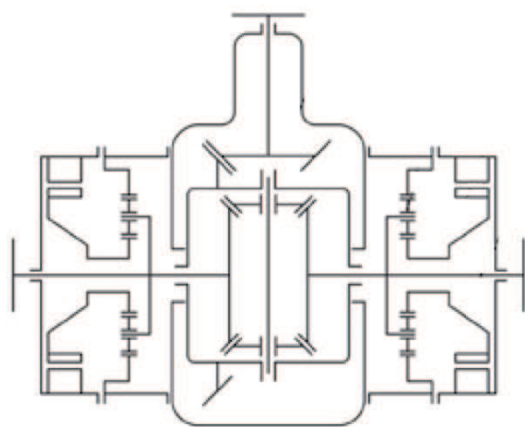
Гибридный несимметричный привод колес разработки НТЦ «Автомобили с КЭУ» [2]
